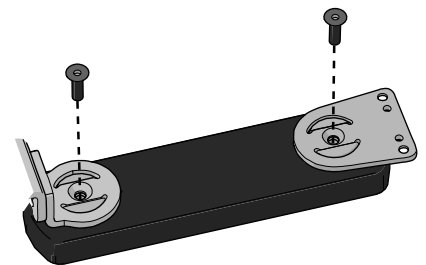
Die Halterung wird durch eine Schraube an jedem Ende des Pulthalters gesichert.
